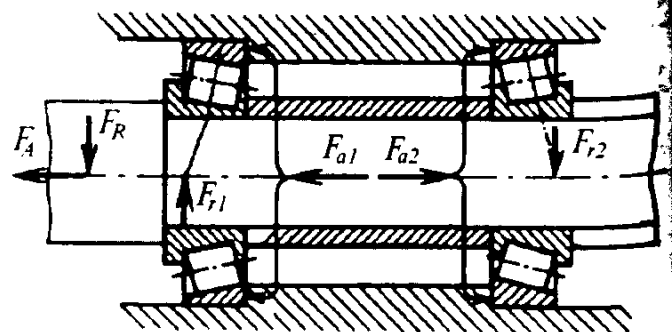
Схема нагружения вала и опор с радиально-упорными регулируемым подшипниками
